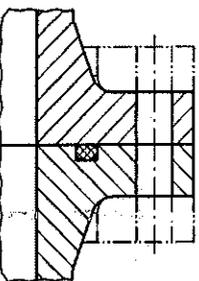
Vorschweißflansch mit O-Ring und Metall-Losflansch
